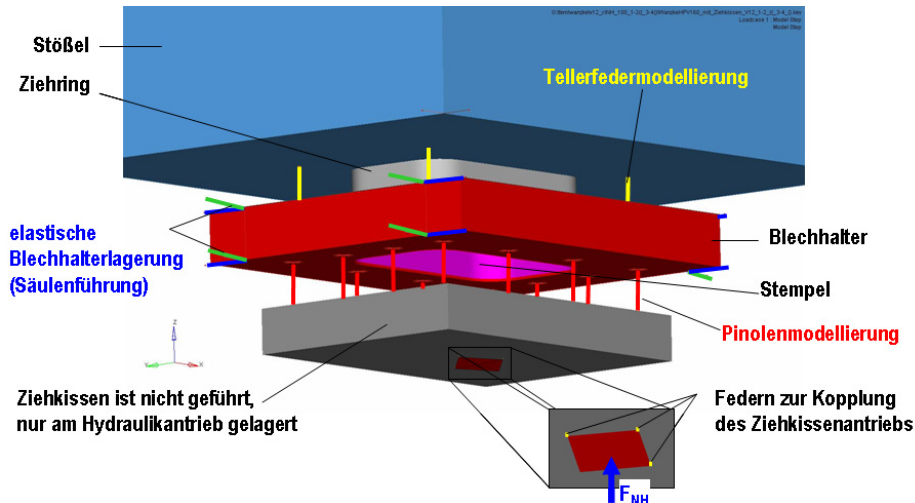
Modellierung des Versuchswerkzeuges einschließlich elastischer Lagerung des Blechhalters und des Ziehkissens
